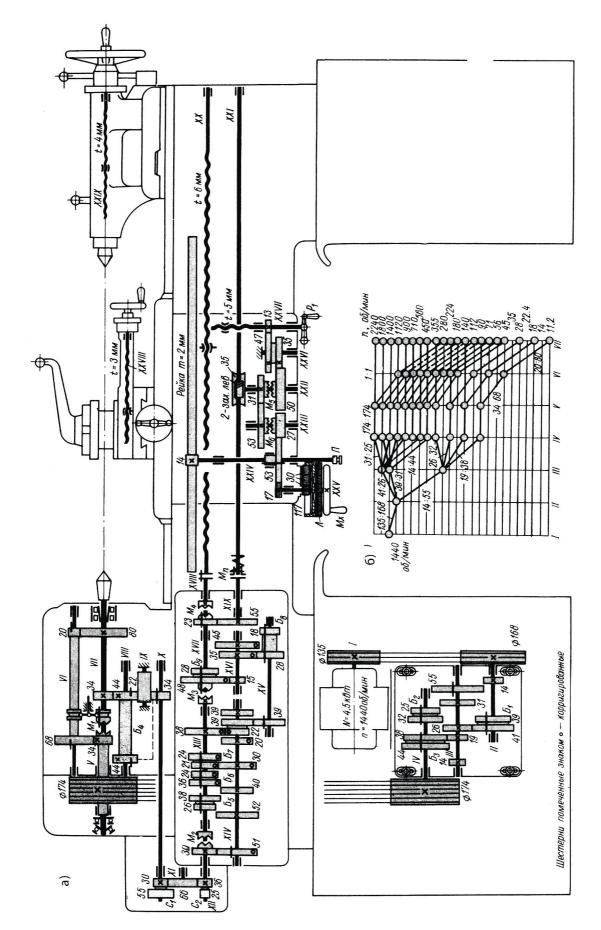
Кинематическая схема токарно-винторезного станка 1A616
